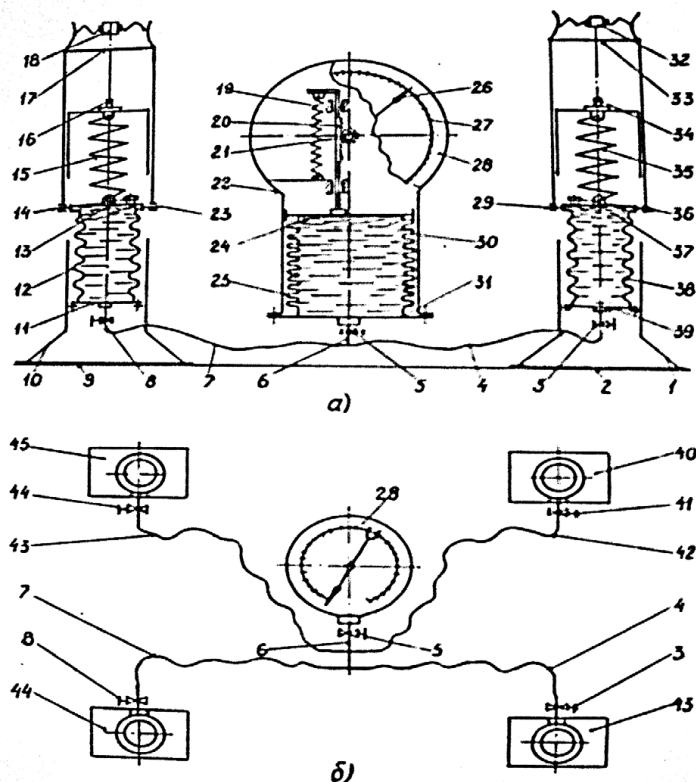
Принципова схема пристрою для зважування багатоопорних рухомих об'єктів.
